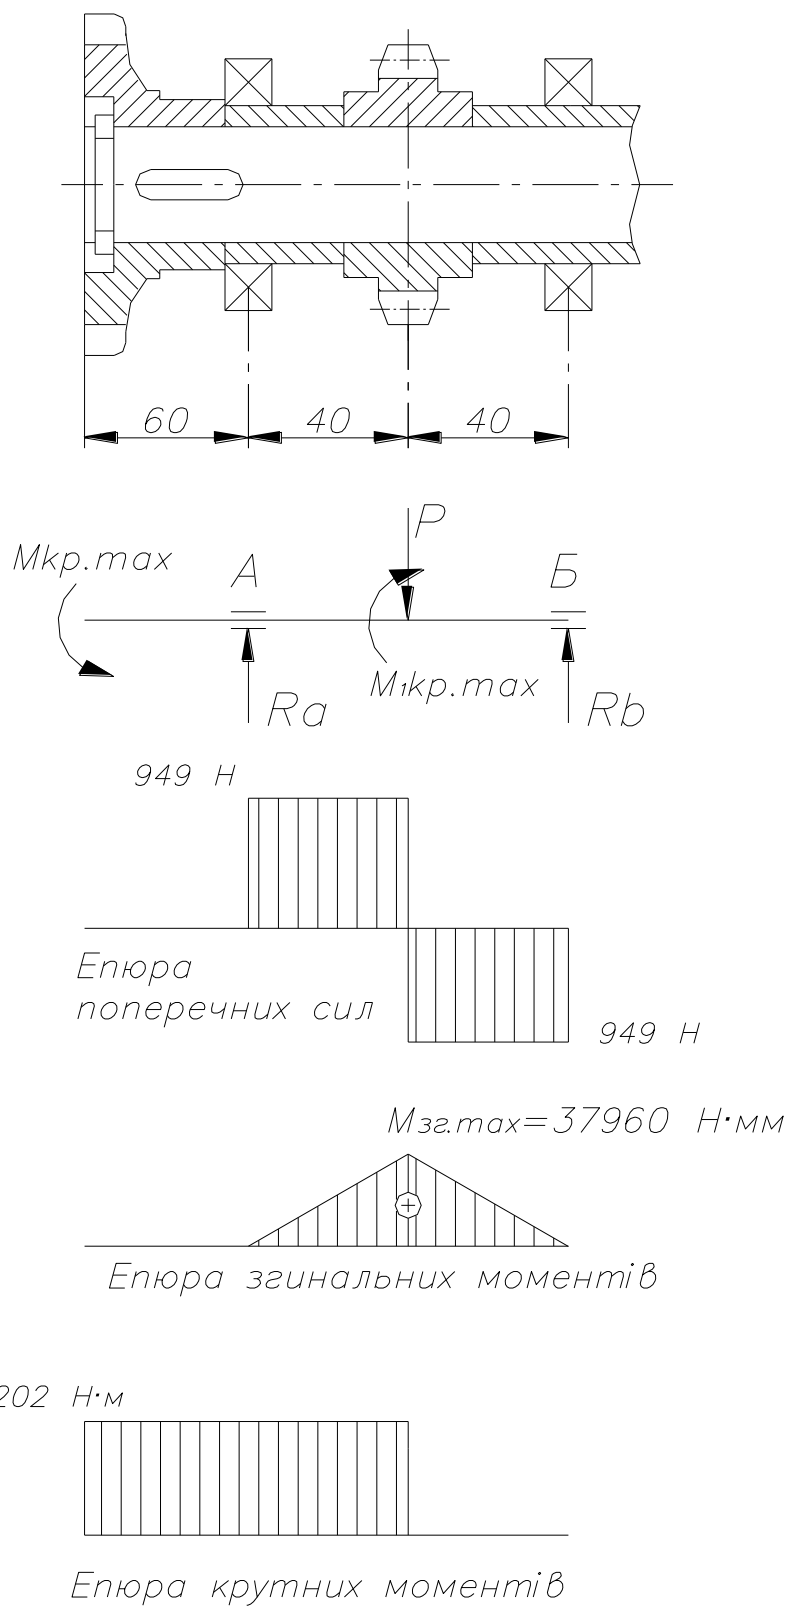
Розрахункова схема і епюри моментів ведучого вала ланцюгового редуктора приводу роторного копача
